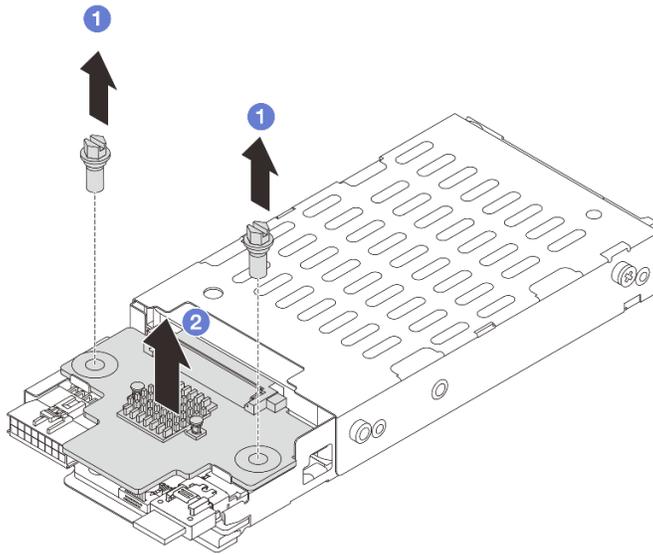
Retrait du fond de panier d'unité 7 mm (haut)
